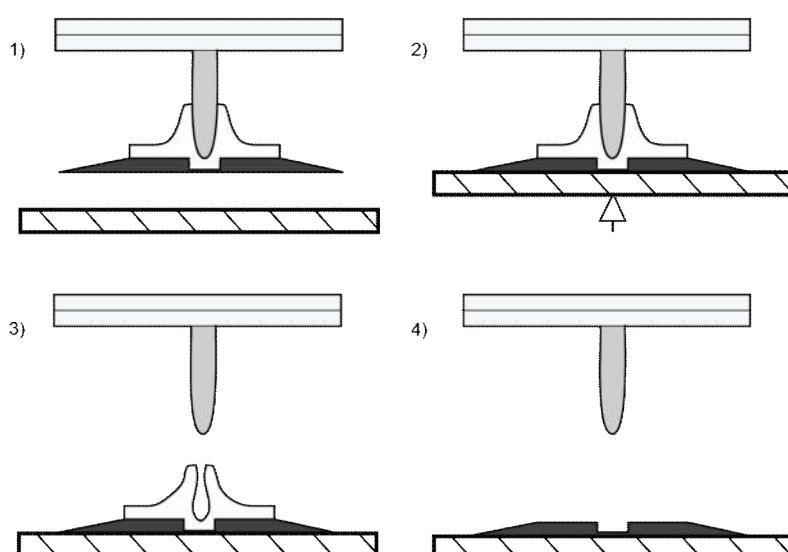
Процесс подготовки штанц-формы к высечке
